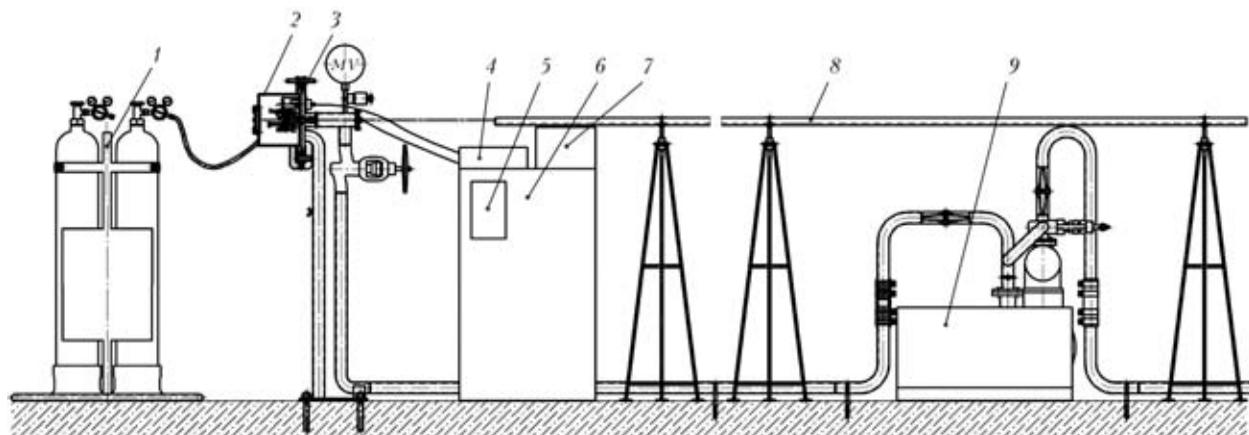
Схема станда для сварки GTAW стыкозамковых соединений ПЭЛов: 1 — стойка газобаллонная; 2 — сварочная камера; 3 — головка сварочная АДЦ 627.03.00.000; 4 — коллектор АДЦ 625.07.00.000; 5 — пульт управления выносной ИЦ 616.30.00.000; 6 — источник питания ИЦ 616.УЗ.1; 7 — блок контроллера ИЦ 616.20.00.000; 8 — ложемент; 9 — агрегат вакуумный золотниковый
